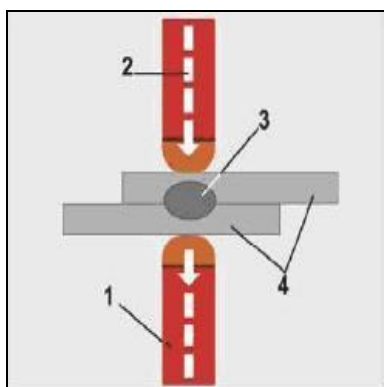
Схема сварного точечного соединения: 1 – электрод; 2 – электрический ток; 3 – ядро; 4 – свариваемый материал
